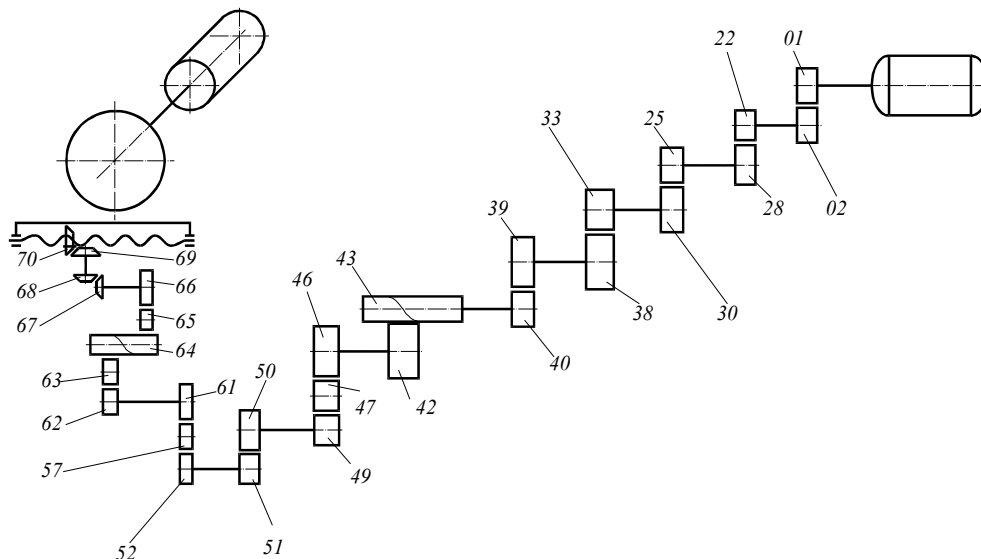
Кинематическая схема установки циркуляционного трения: 01 – 70 шестерни
